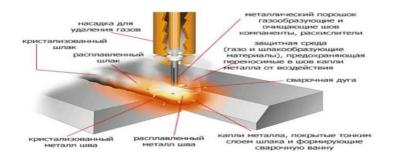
Сварка самозащитной порошковой проволокой
